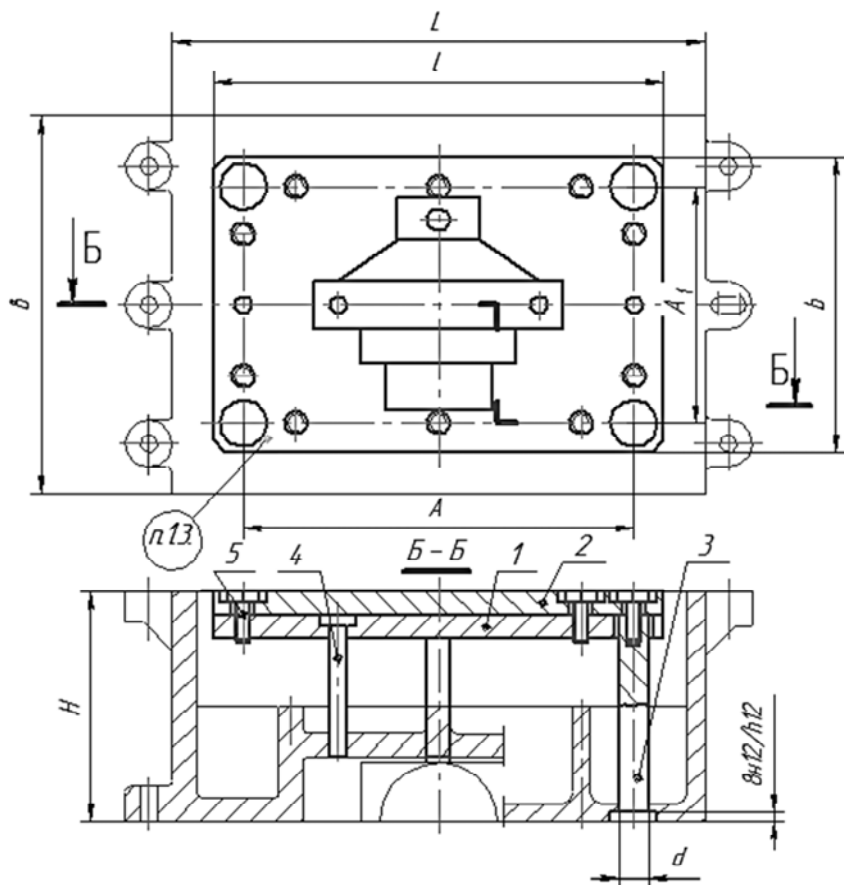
Приспособление для выталкивания отливок из металлической формы с параллельным разъемом:
